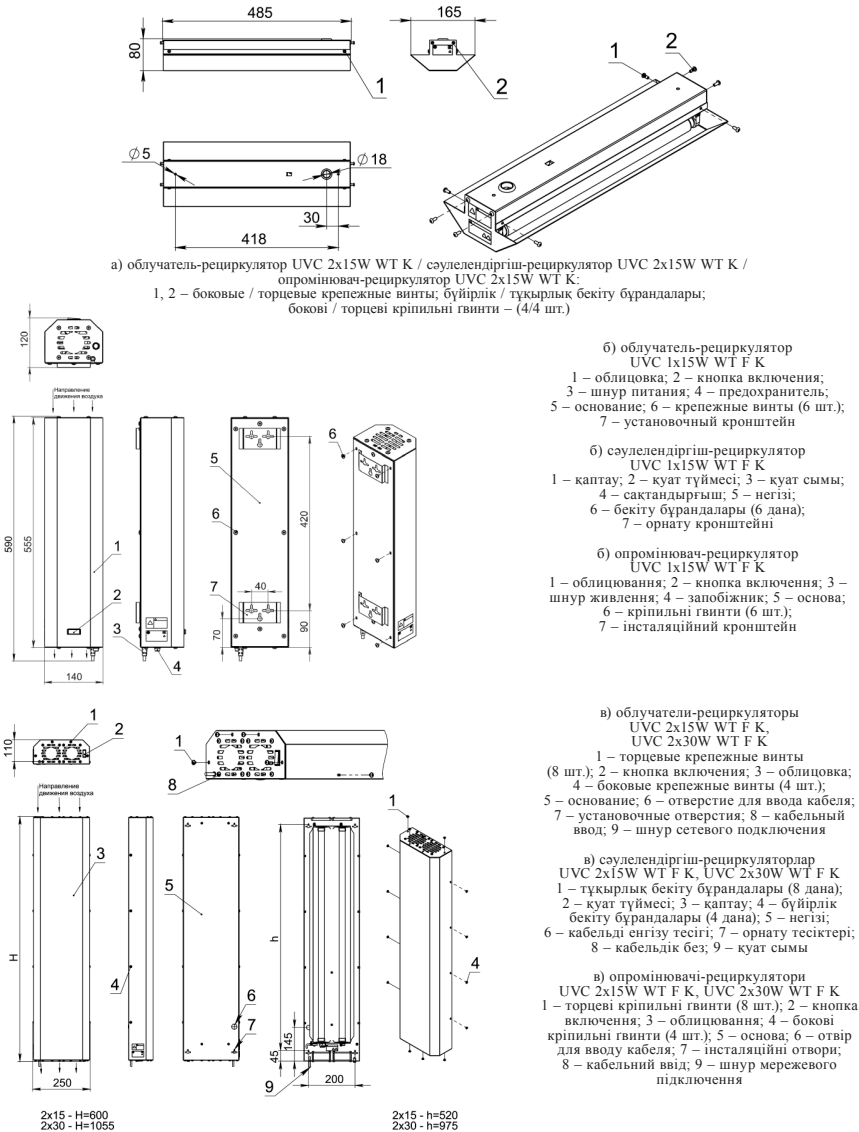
Общий вид и основные размеры облучателей-рециркуляторов
